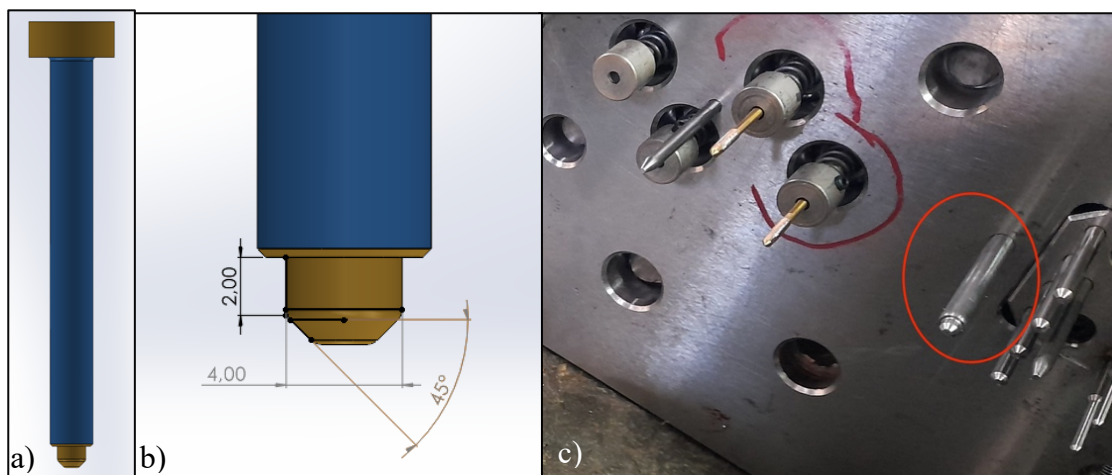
Calcadores: a) Desenho do calcador visto de perfil; b) Dimensões da zona maquinada do calcador e c) Calcador maquinado já aplicado na ferramenta.
